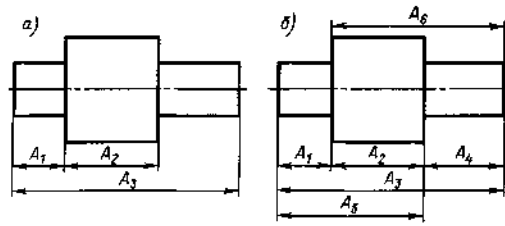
Постановка размеров конструктором (а) и технологом (б)
